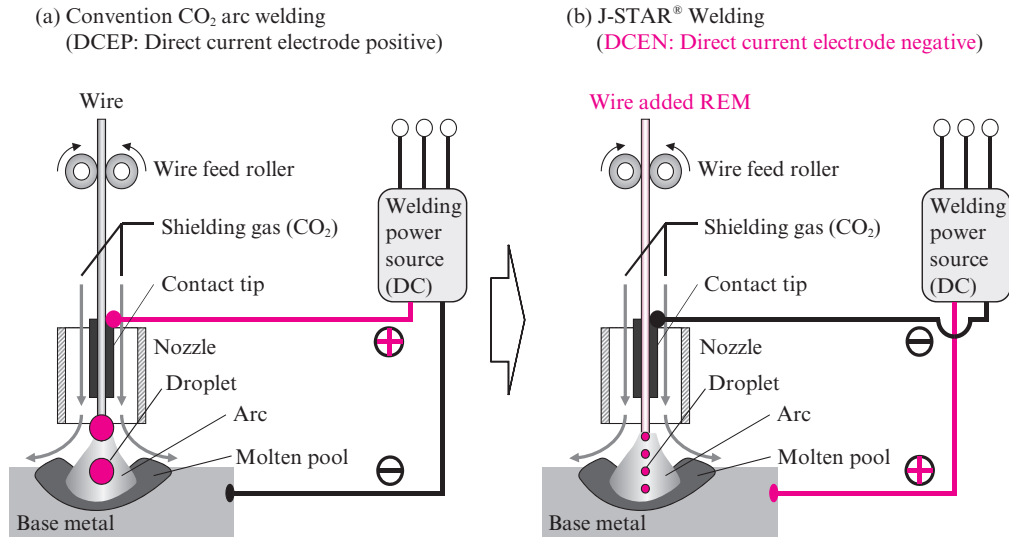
従来の炭酸ガスアーク溶接と「J-STAR® Welding」の相違
